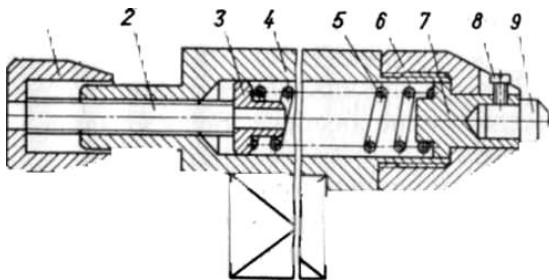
Вигладжувач для обробки зовнішніх циліндричних поверхонь
